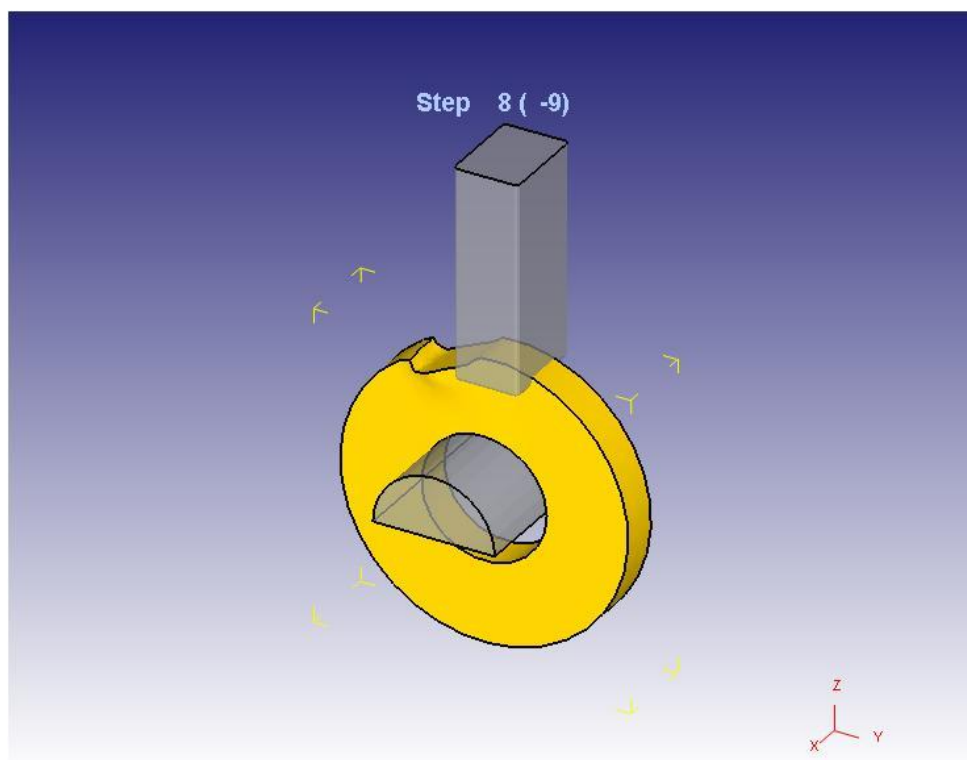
Положение заготовки после операции поворота вокруг оси X
